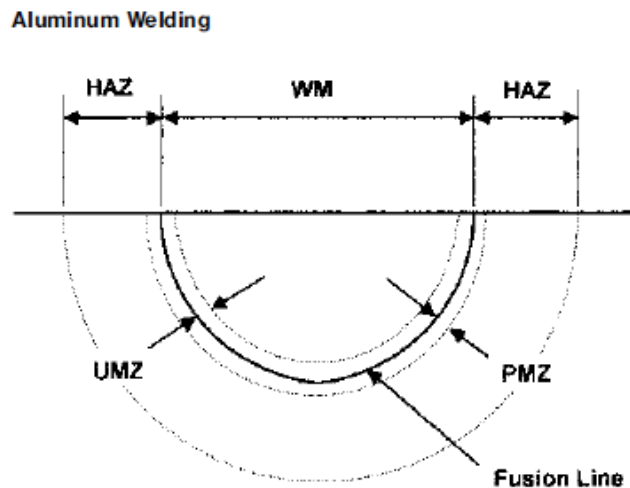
Definición de las diferentes zonas en una soldadura de aluminio. [1]
